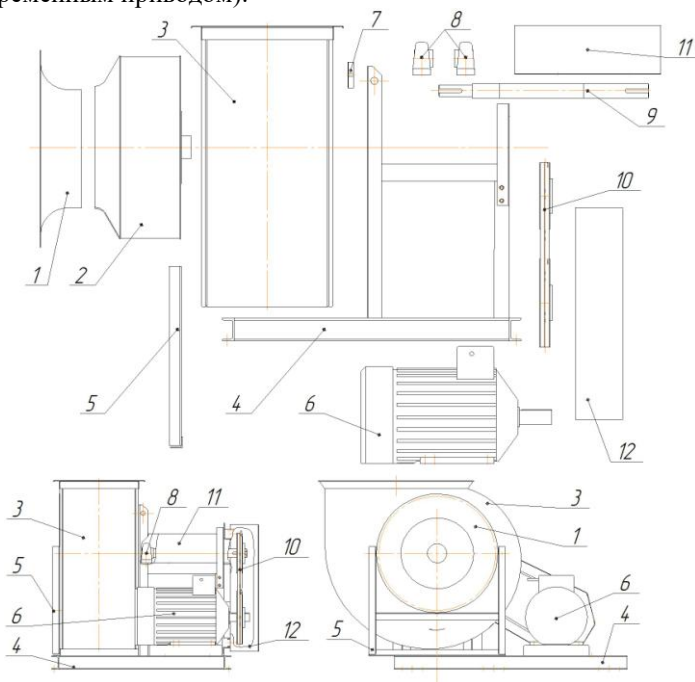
устройство центробежных вентиляторов 5-й конструктивной схемы (с ременным приводом).
